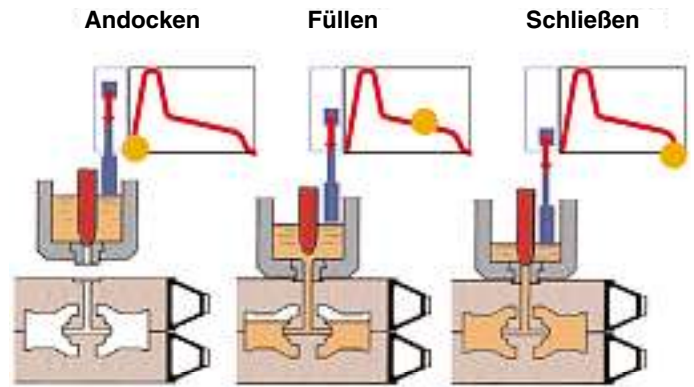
Kontaktgießen: Steuerung des Gießablaufs
